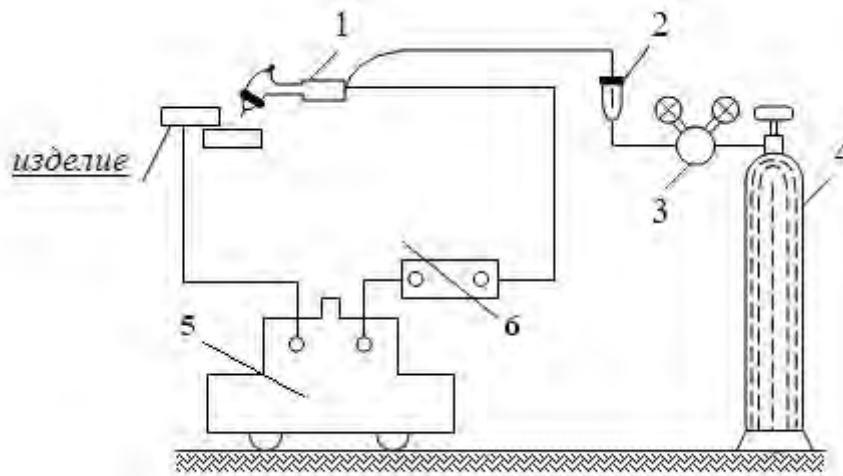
Схема сварочного поста для ручной дуговой сварки в защитных средах
